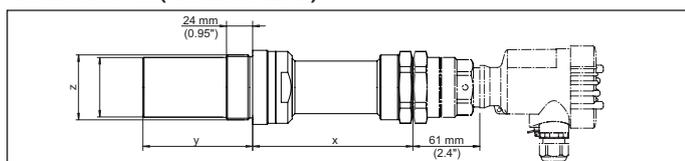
Montageadapter mit Tubus (optional) für frontbündige Montage, für VEGAMIP mit innenliegender Hornantenne, Gewindeausführung G1½ mit PTFE-Abdeckung (auch mit 1½ NPT-Gewinde)
